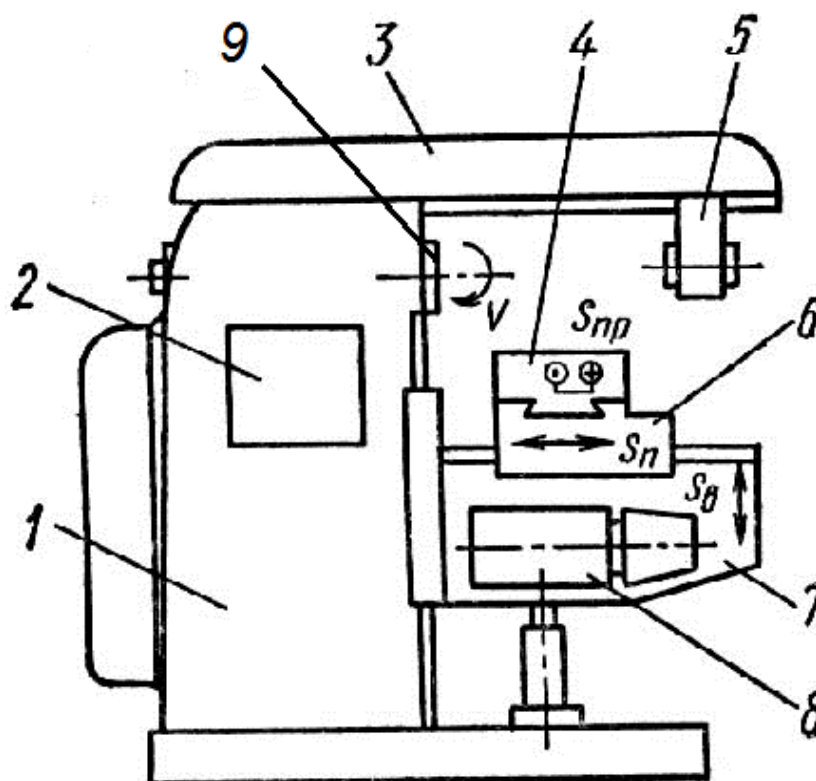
Общий вид горизонтально-фрезерного станка:
